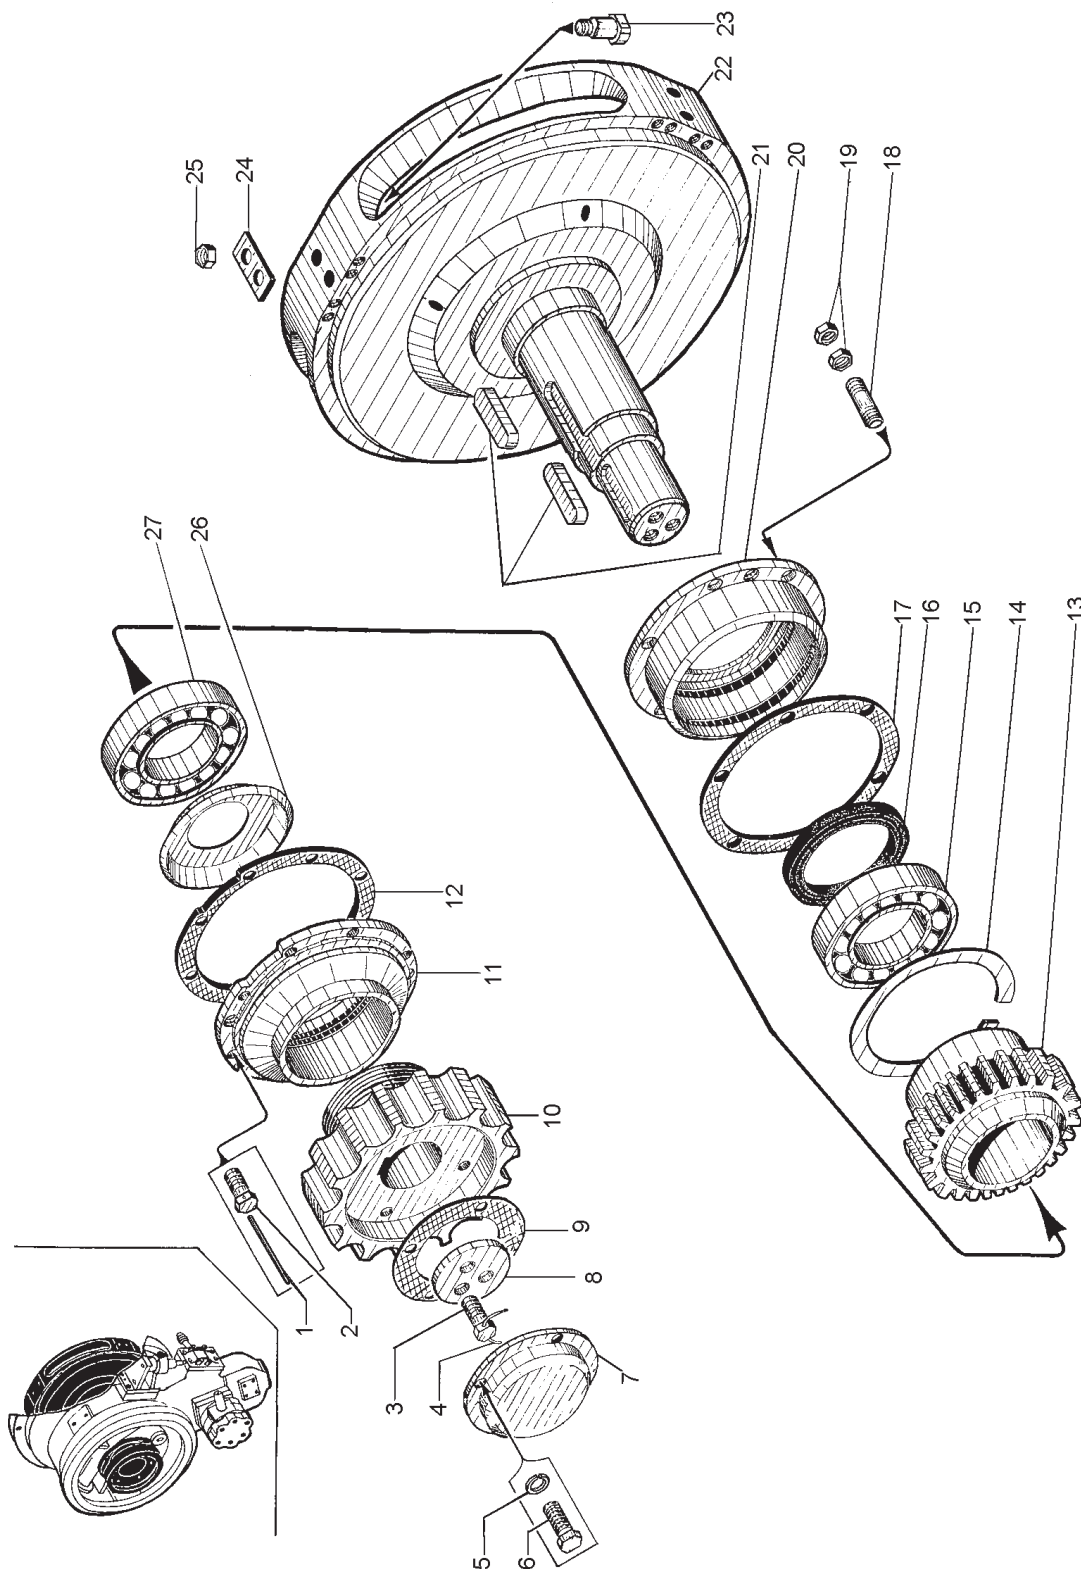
Редуктор промежуточный (ДЗ-98.10.06.000-09)
